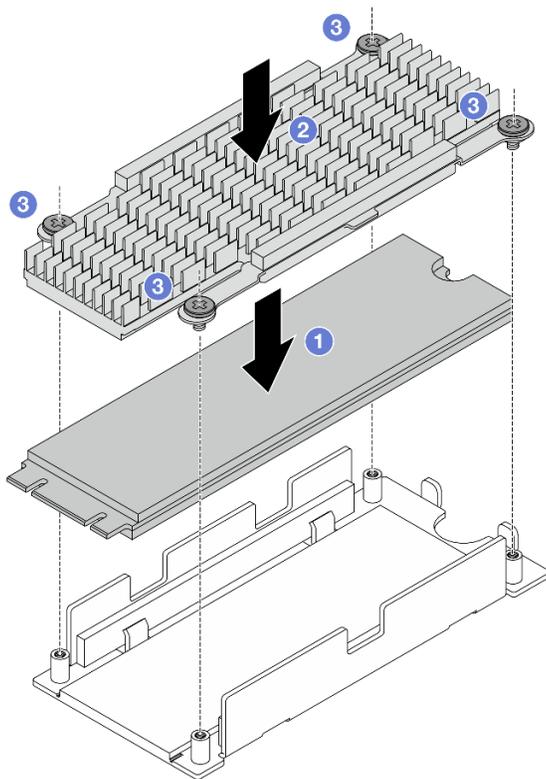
Assemblage du dissipateur thermique et de l'unité M.2
